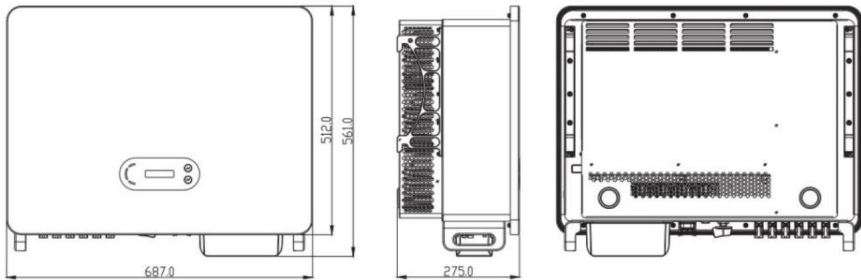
Avant, côté et arrière de la machine (80KW)
